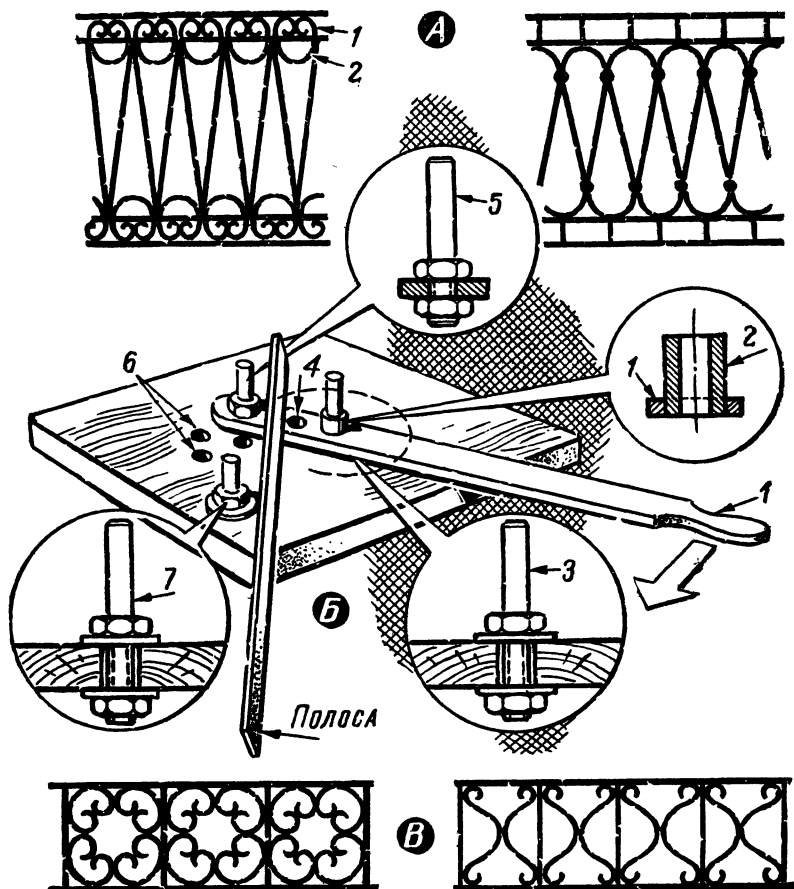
Поделки из полосового железа: А — ограды; Б — гибочное приспособление: 1 — рычаг; 2 — втулка, 3 — штырь; 4 — отверстия; 5 — штырь; 6 — отверстия; 7 — штырь-упор; В — каминные решетки.
